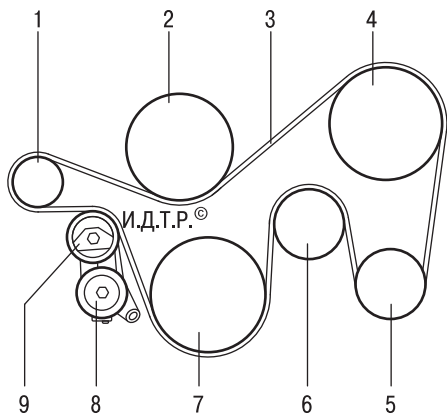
Ремень привода вспомогательных агрегатов: 1 – шкив генератора; 2 – шкив водяного насоса; 3 – поликлиновой ремень привода вспомогательных агрегатов; 4 – шкив насоса гидросилителя; 5 – шкив компрессора кондиционера; 6 – направляющий ролик; 7 – шкив коленчатого вала; 8 – автоматический натяжитель ремня; 9 – ролик автоматического натяжителя
